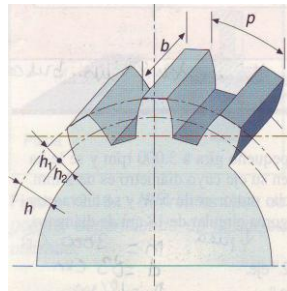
Engranaje De Dientes Rectos [Shigley 1990]
